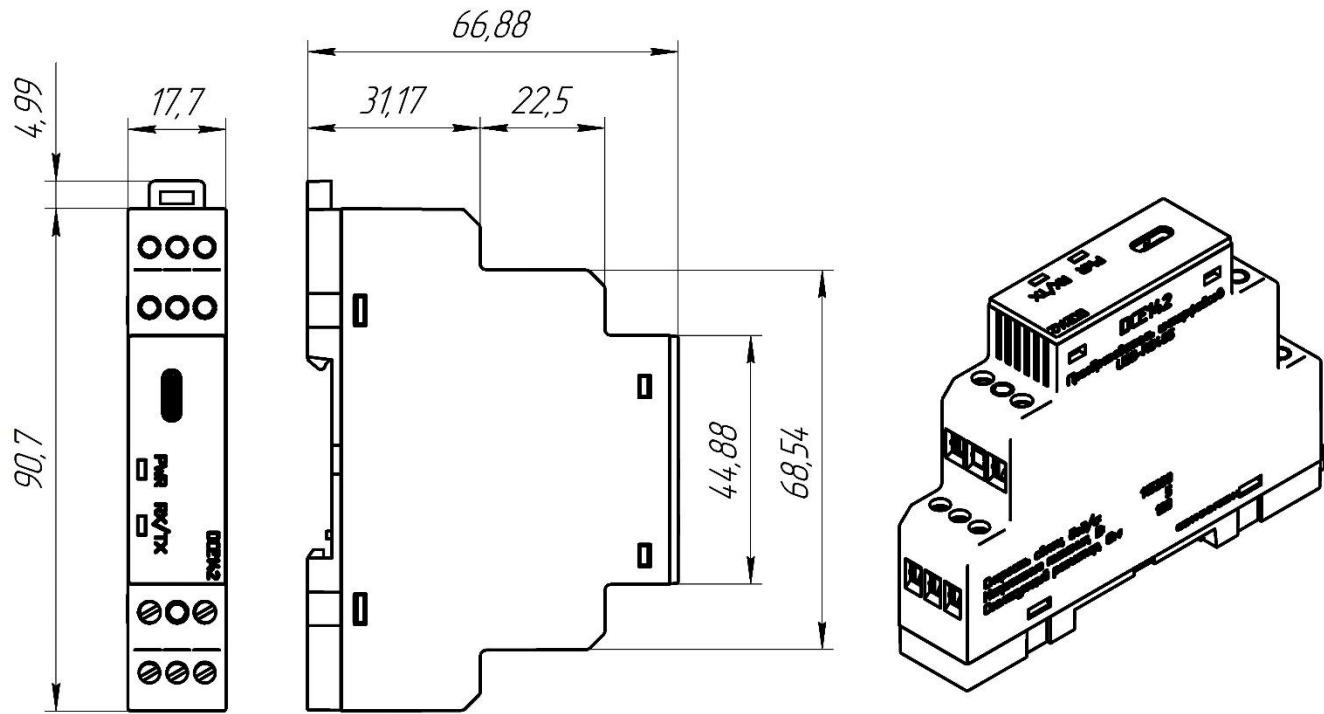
Габаритные размеры корпуса преобразователя интерфейсов USB-RS485 DCE142
